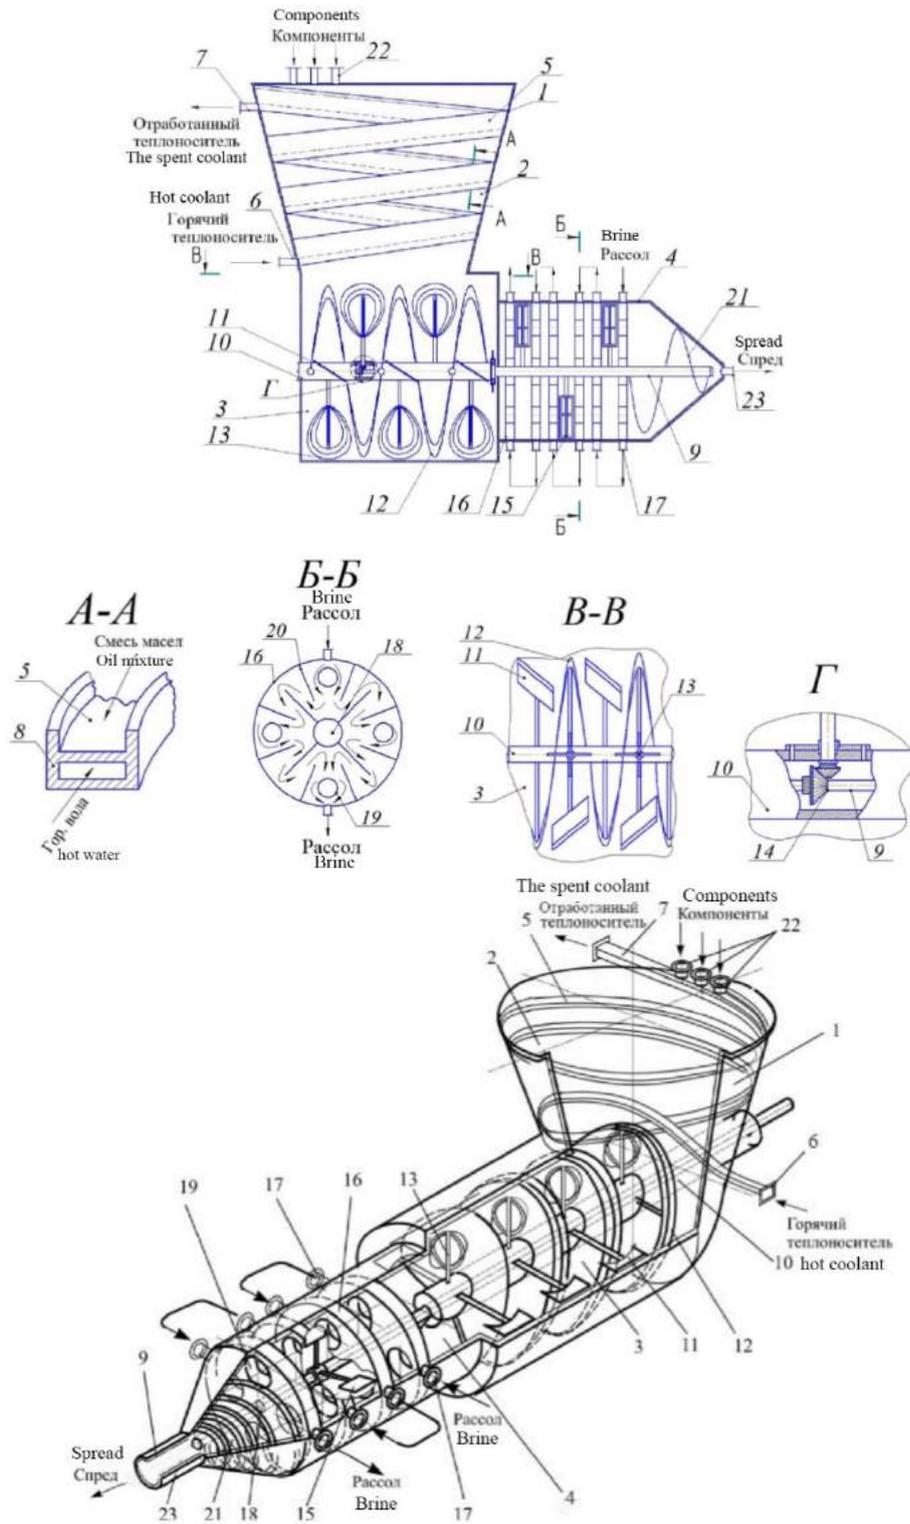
Эмульсер. 1 – вертикальный корпус; 2 – греющая камера; 3 – смешивная камера; 4 – винтовой полый лоток; 5, 6 – патрубков; 7 – выступы; 8 – цилиндрическая камера; 9, 10 – тихоходный и быстроходный валы; 11 – скребки; 12 – ленточная спираль; 13 – вертикальные венчиковые смесители; 14 – коническая зубчатая передача; 15 – скребки; 16 – теплообменные пластины; 17 – патрубков; 18 – центральное отверстие теплообменной пластины; 19 – секторное отверстие; 20 – секторные перемычки; 21 – нагнетающий шнек; 22 – загрузочные патрубки; 23 – выгрузочное отверстие
